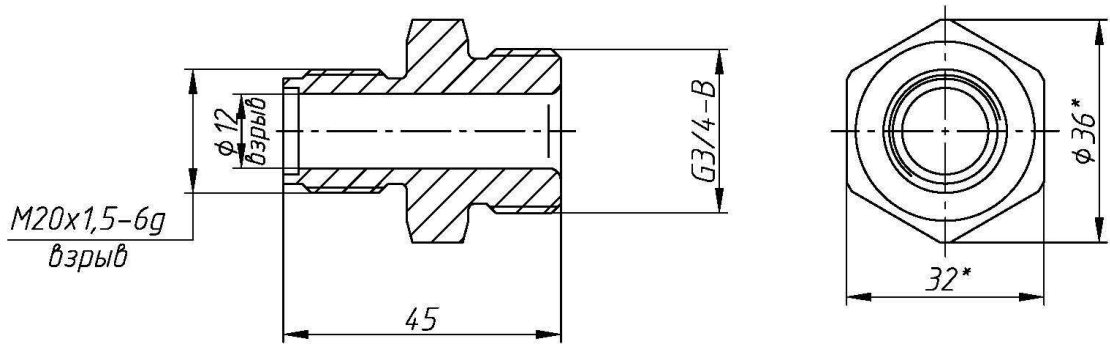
Штуцер ЗАО НПК ЭТАЛОН для прокладки кабеля в трубе с соединительной резьбой G3/4-B
